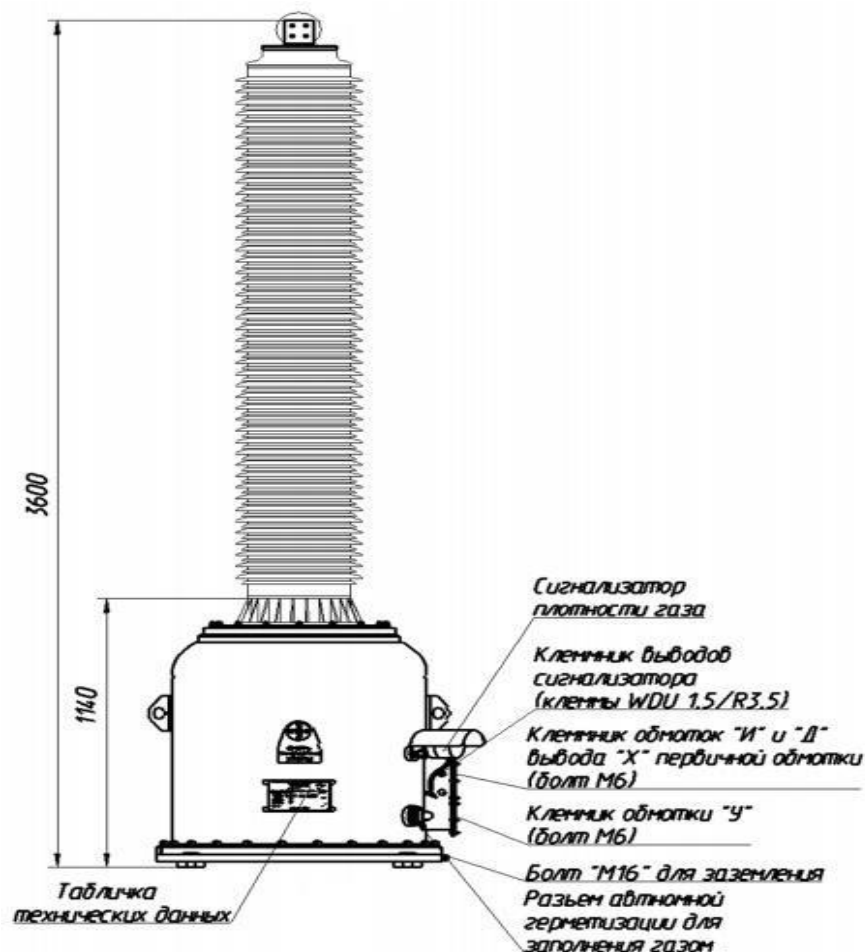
Габаритные размеры трансформатора напряжения ЗНГ-220 с полимерным изолятором
